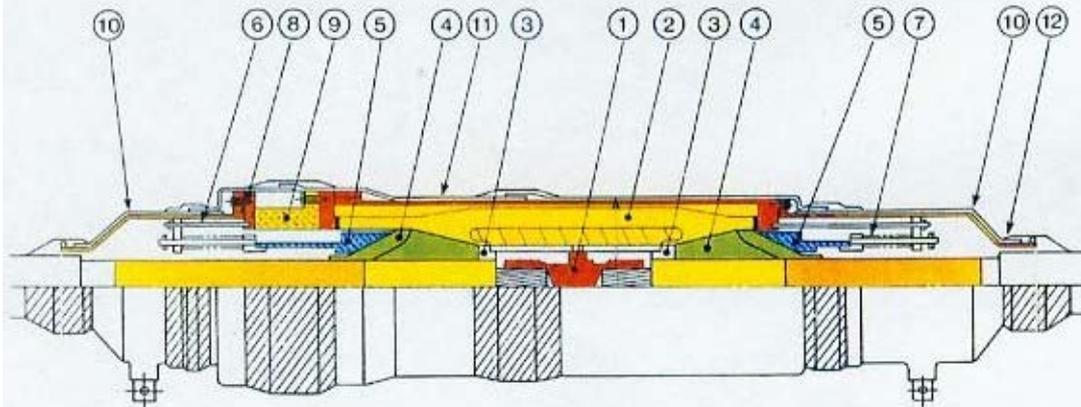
Premolded one-piece type joint (SPJ)電纜接續匣之構造
